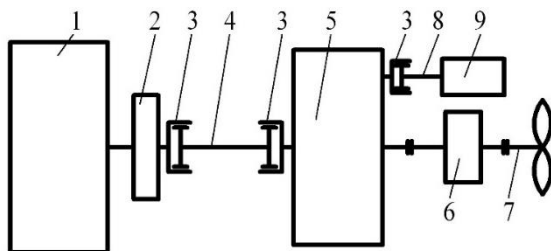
Кінематична схема трансмісії судна з ДРА: 1 – дизельний двигун; 2 – маховик; 3 – зубчасті муфти; 4 – ресора; 5 – редуктор; 6 – ГУП; 7 – гребний вал; 8 – вал привода; 9 – генератор
